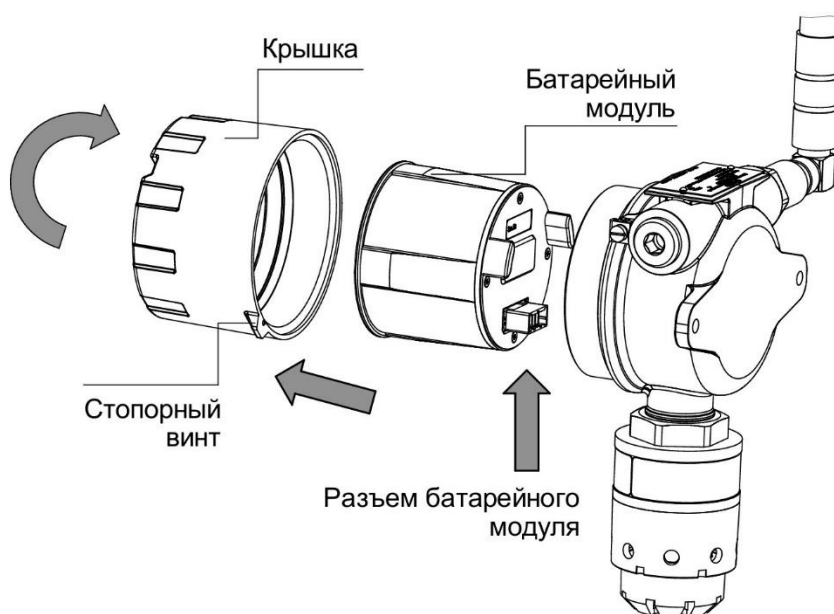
Схема разбора газоанализатора для активации (вид сзади)
